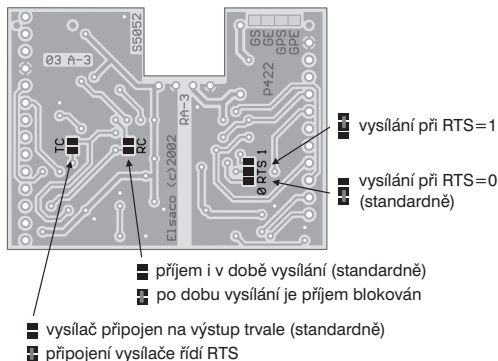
Převodník s modulem P232GPS (EI6011/6012.90)
